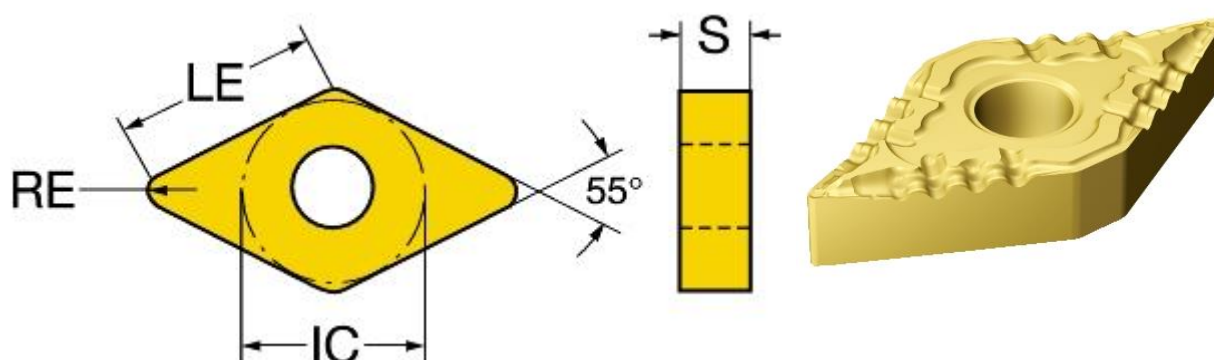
Пластина твердосплавна для чистового та остаточного точіння DNMG 11 04 12-PF LC25
